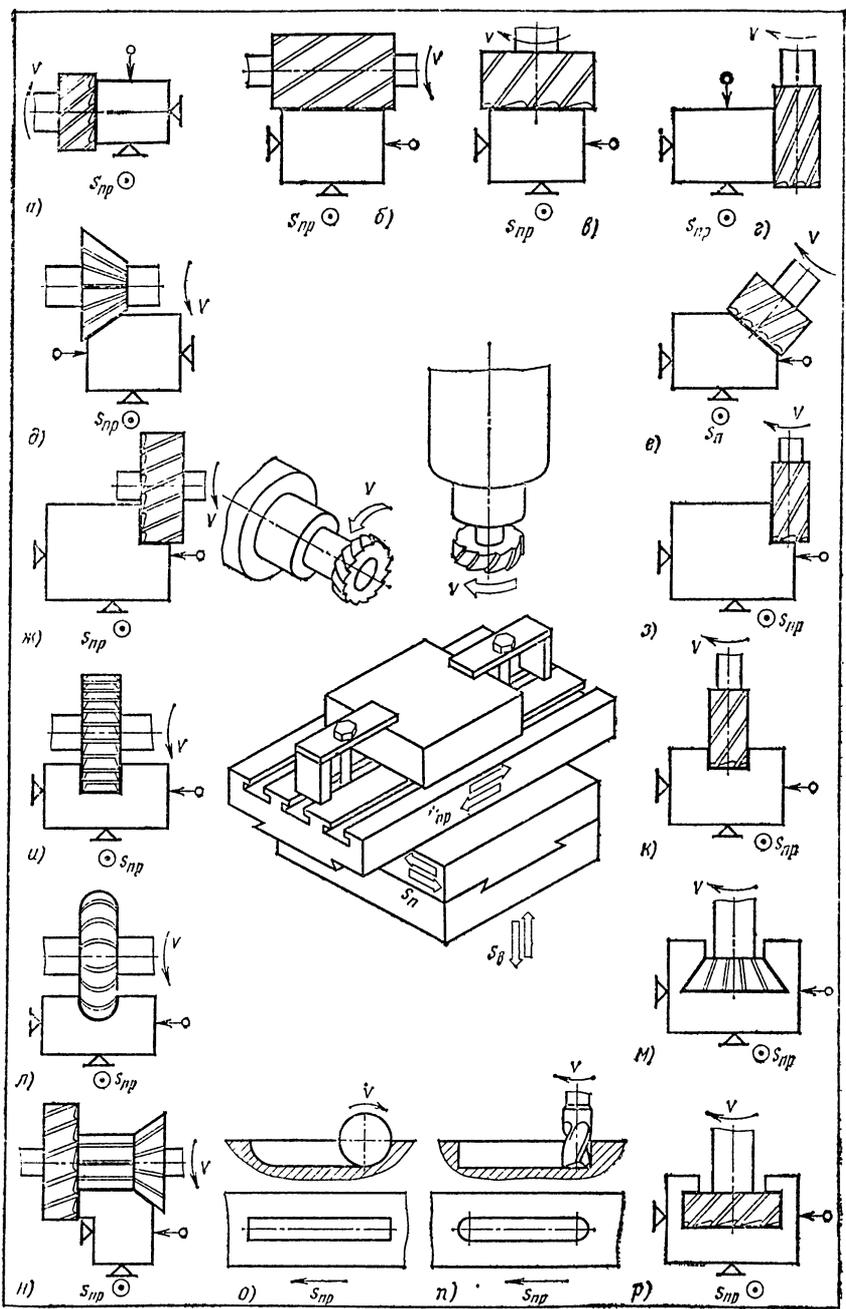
Схемы обработки поверхностей на универсальных фрезерных станках
